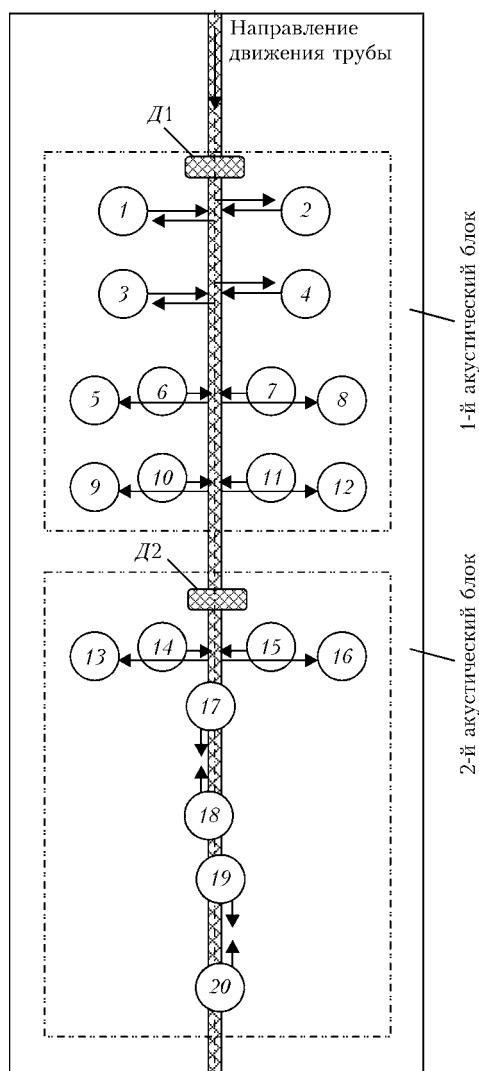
Схема расположения ПЭП для контроля продольных сварных соединений труб диаметром 508...1420 мм и толщиной стенки 7...50 мм: D1 и D2 — лазерные датчики слежения за валиком усиления сварного шва; 1-4 — группа наклонных УЗ преобразователей; 5-16 — УЗ преобразователи, работающие в tandemных схемах; 17-20 — УЗ преобразователи, стоящие на сварном шве и работающие в иммерсионном варианте на обнаружение поперечных дефектов
